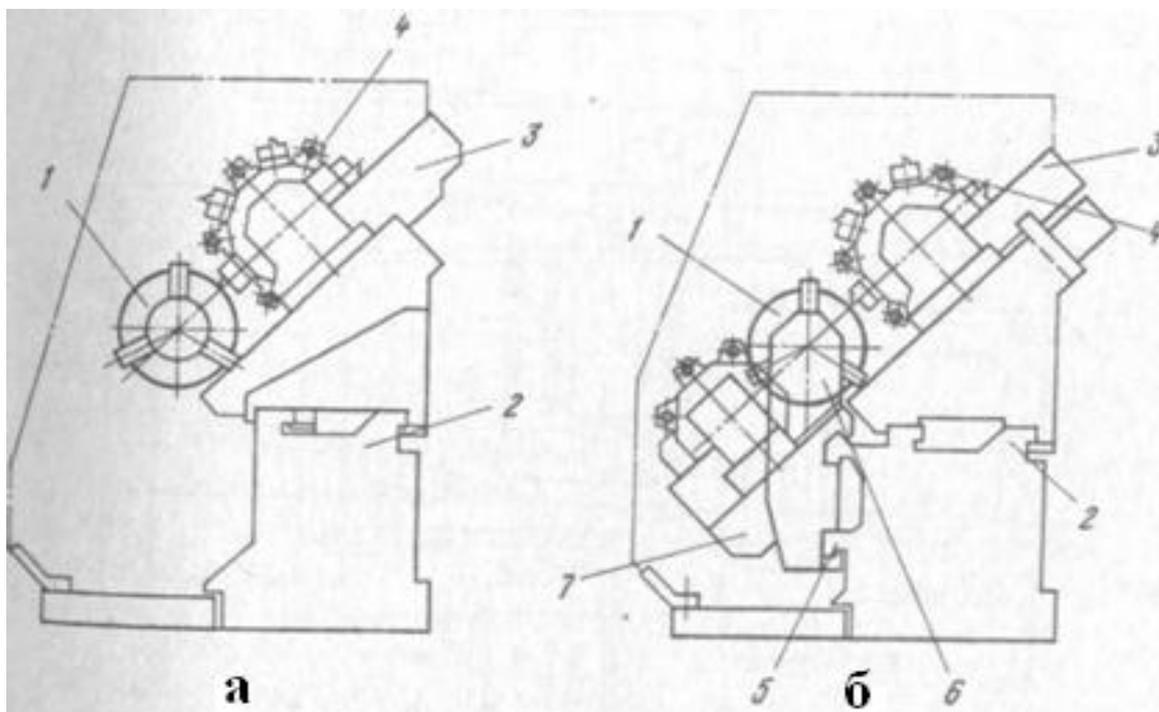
Угловая компоновка токарных станков с ЧПУ: а – с одним суппортом, б – с двумя суппортами.
